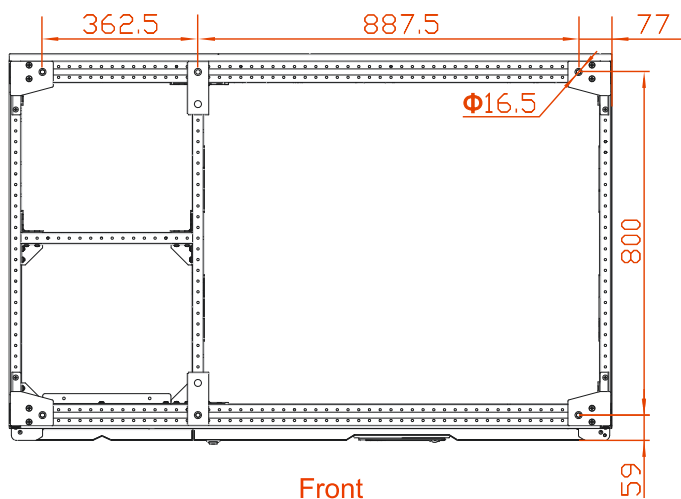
Вид снизу на установочный пьедестал KR33300, KR33400
